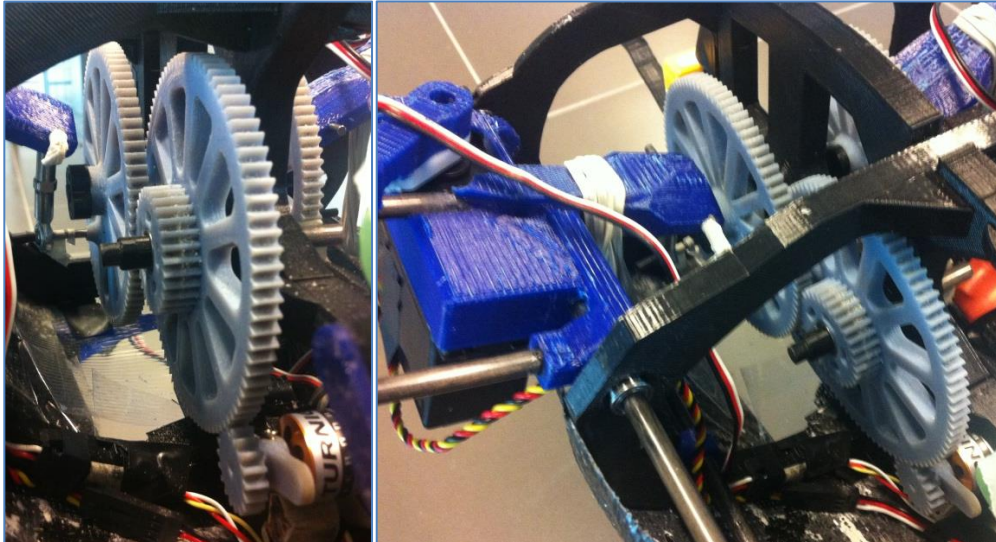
Engranajes unidos al fuselaje y a los hombros.
